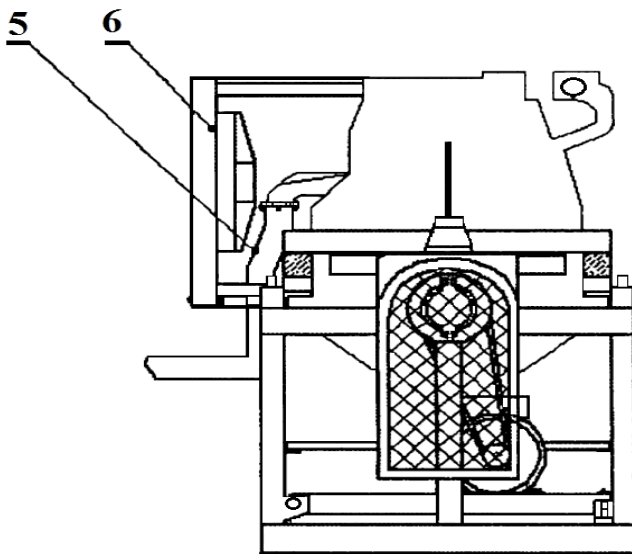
Стенд для обкатки ДВС, вид спереди
